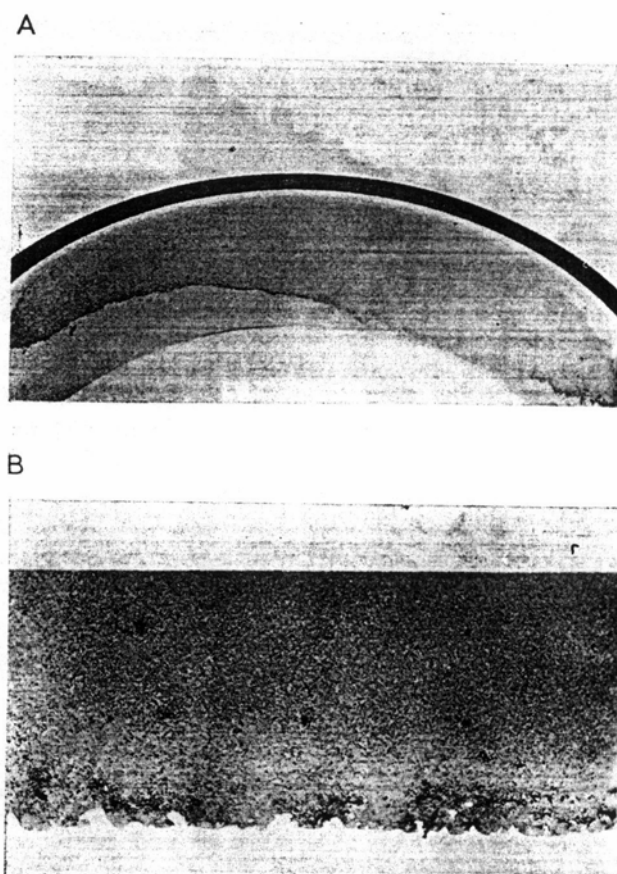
Escamado superficial: A.- tal que aparece sobre una zona muy extendida sobre una pista del anillo exterior del ruleman de rodillos cónicos; B tal que aparece justo sobre la superficie en la forma de pequeñas fisuras horizontales y de escamado en la base de una sección según una cuerda.
